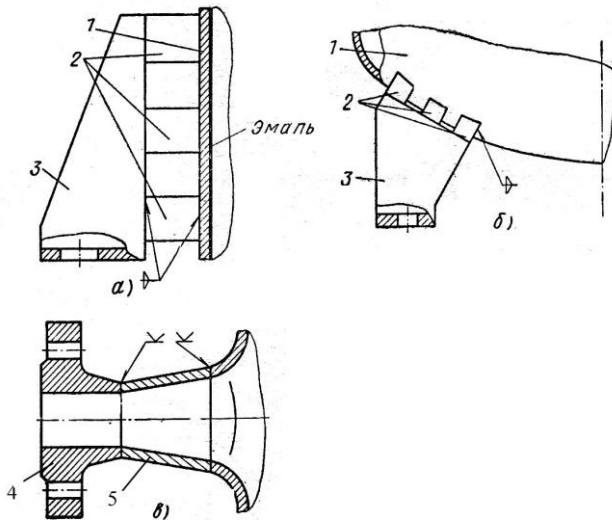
Конструктивное оформление узлов эмалированных аппаратов: а, б – с приварными лапами; в – с приварным штуцером; 1 – корпус; 2 – накладка; 3 – лапа; 4 – фланец штуцера; 5 – конический патрубок штуцера
